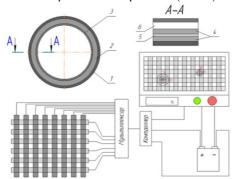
Сенсорный датчик износа поверхности подшипника скольжения
